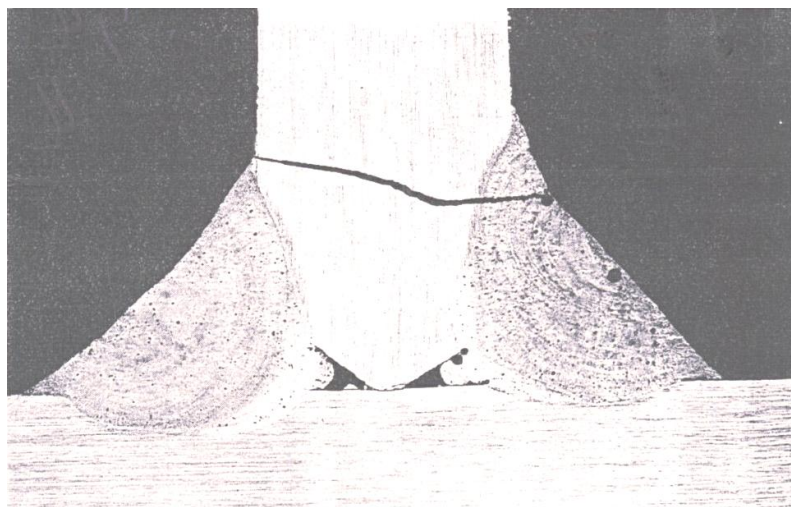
Заваренная трещина усталости в сварном шве у окончания кницы на кромке ребра жесткости в конструкции корпуса танкера [86]
